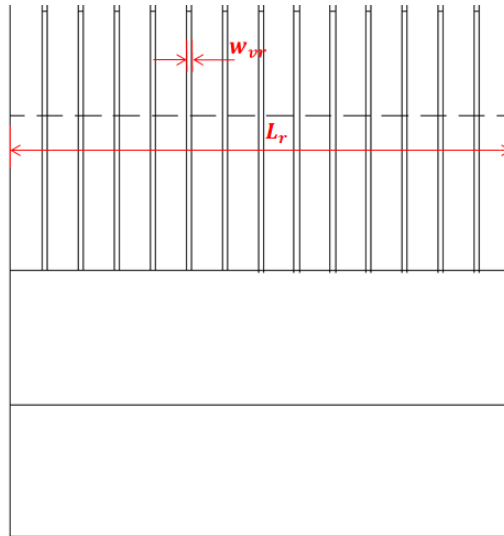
Corte com as principais variáveis dimensionais do rotor
